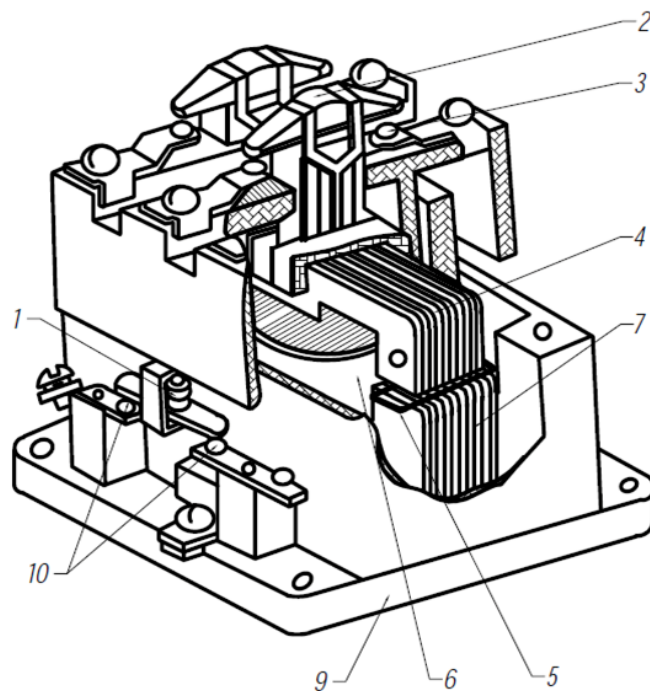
Магнітний пускач серії ПМА: 1 — пружина; 2 — рухомі контакти; 3 — нерухомі контакти; 4 — якір; 5 — короткозамкнений виток; 6 — котушка; 7 — осердя; 9 — основа
